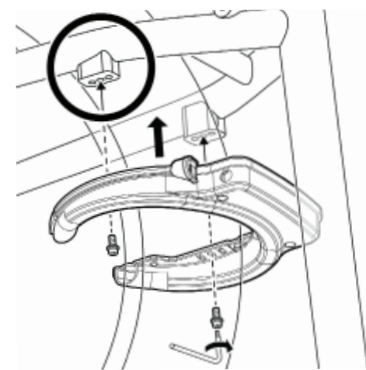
Instale pernos con arandelas cautivas; posición de montaje del marco n.º 1
